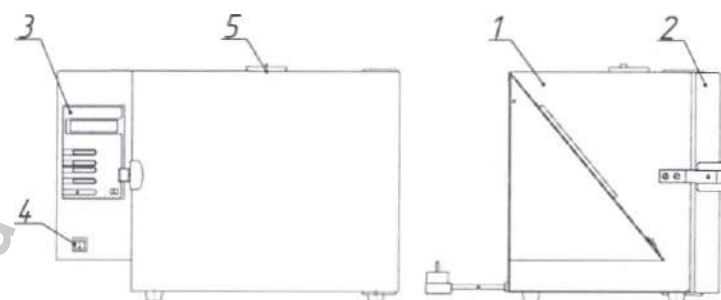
Общий вид ШСвЛ-40 КИУС.941729.003-07.
